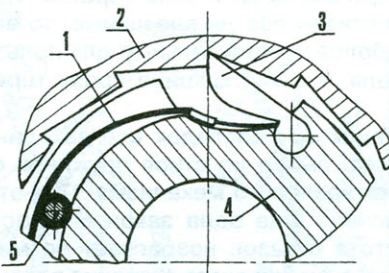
Схема установки сборной пружины: 1 — пружина; 2 — корпус механизма, наружный; 3 — собачка; 4 — корпус механизма, внутренний; 5 — ось пружины.
